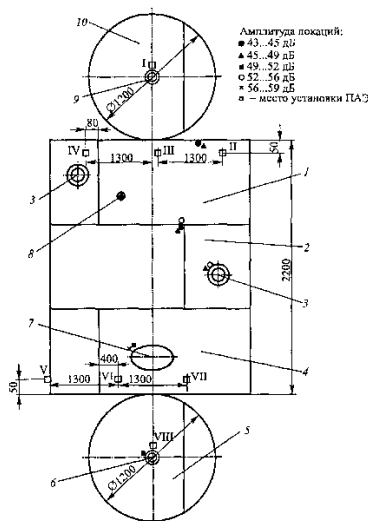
Схема расположения источников АЭ на развертке сосуда и местоположение зарегистрированных дефектов: 1 — обечайка 1; 2 — обечайка 2; 3 — вход воздуха; 4 — обечайка 3; 5 — днище нижнее; 6 — штуцер слива конденсатора; 7 — лазовое отверстие; 8 — штуцер манометра; 9 — штуцер предохранительного клапана; 10 — днище верхнее; I—VIII — номера приемников АЭ
